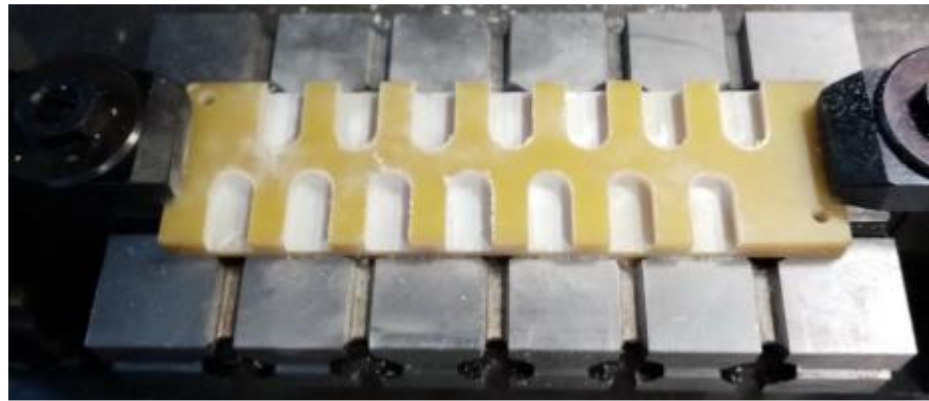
Зразок, оброблений кінцевим фрезеруванням без притискної пластини
